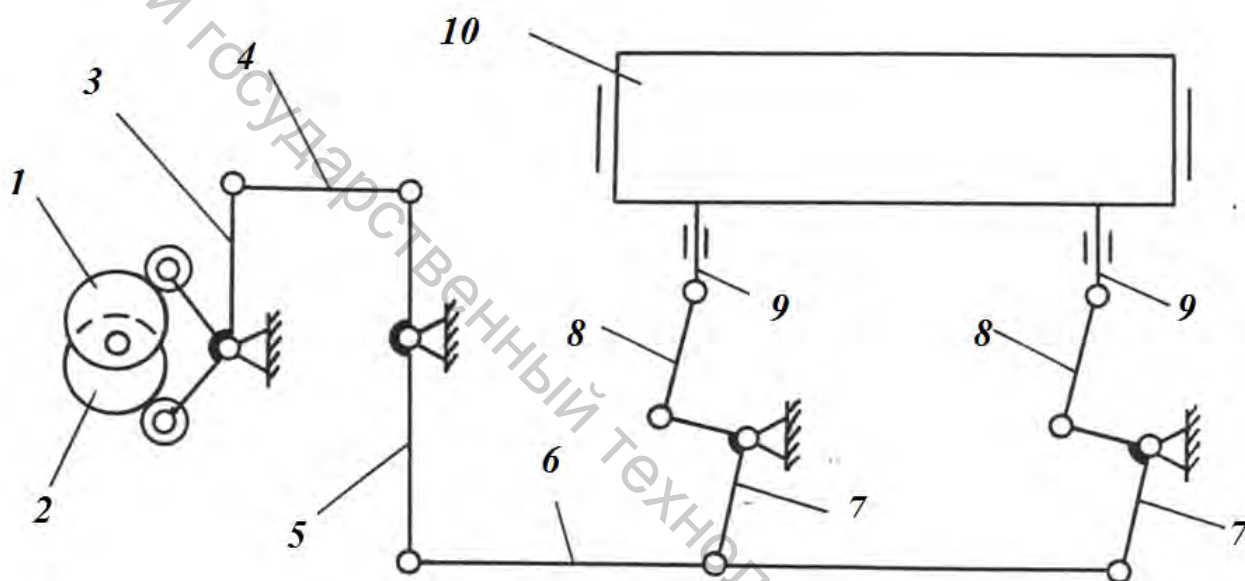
Зевобразовательный механизм станков СТБ
